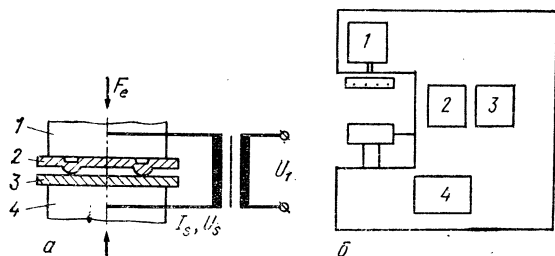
Принцип сварки: а — принцип (1, 4 — электроды; 2 — заготовка с рельефом; 3 — заготовка без рельефа); б — схема (1 — гидравлический цилиндр с блоком управления; 2 — сварочный трансформатор; 3 — электронное управление; 4 — гидравлическая система для обеспечения прижатия)
